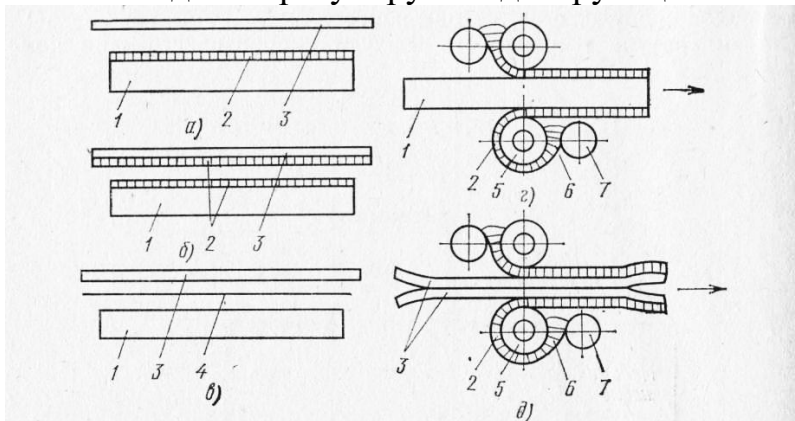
Способы нанесения клея и клеящей пленки: а — клея на одну склеиваемую поверхность, б — клея на обе склеиваемые поверхности, в — клеящей пленки, г — двустороннее механизированное, д — одностороннее механизированное; 1, 3 — детали, 2 — клеевой слой, 4 — клеящая пленка, 5 — обрезиненные вальцы, 6 — ванна с клеем; 7 — дозирующие вальцы
